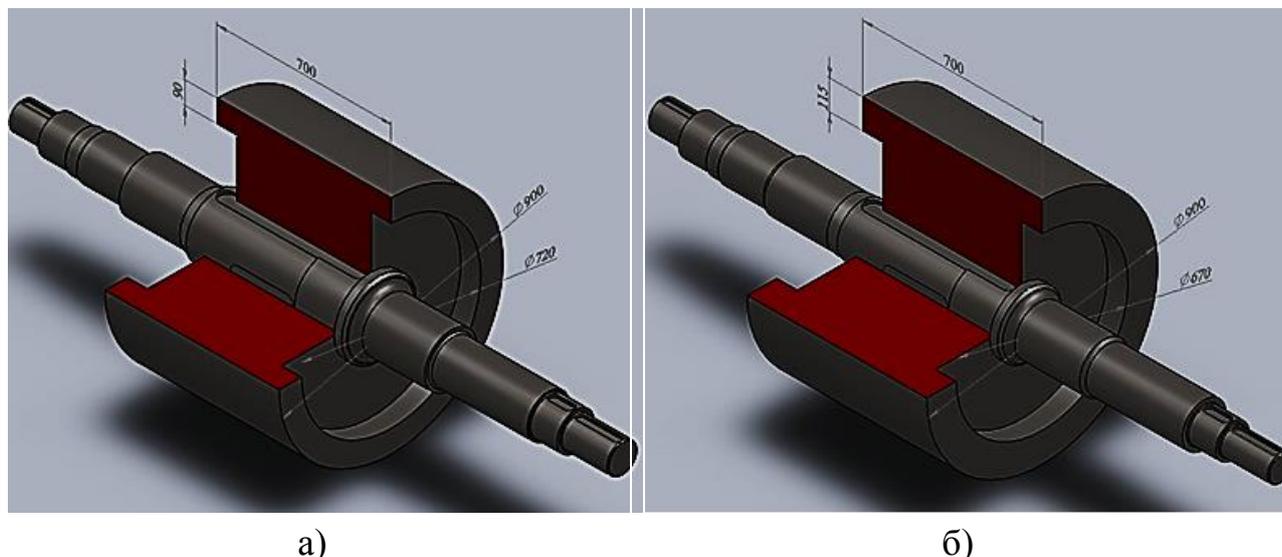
Схематическая трехмерная модель вала со ступицей и бандажом четырехвалковой дробилки:
